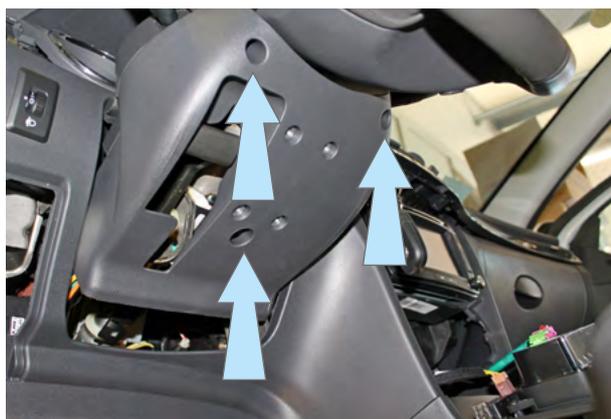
Кожух рулевого вала. Саморезы крепления
